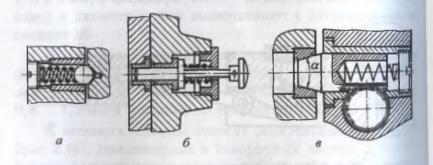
Типовые конструкции фиксаторов: a — шариковый; δ — цилиндрический; ϵ — конический
